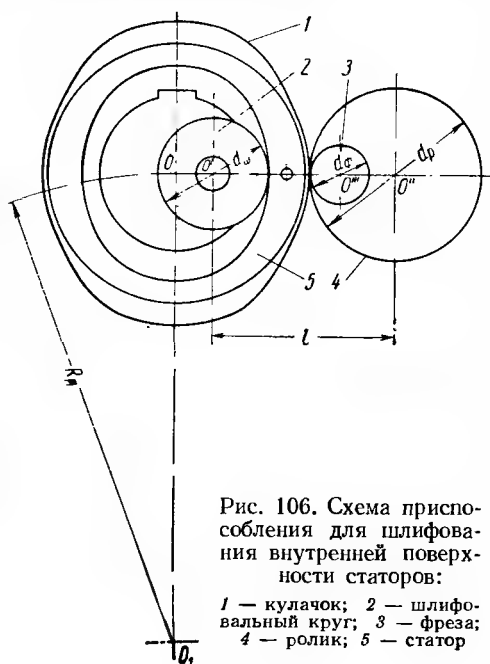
Схема приспособления для шлифования внутренней поверхности статоров:
